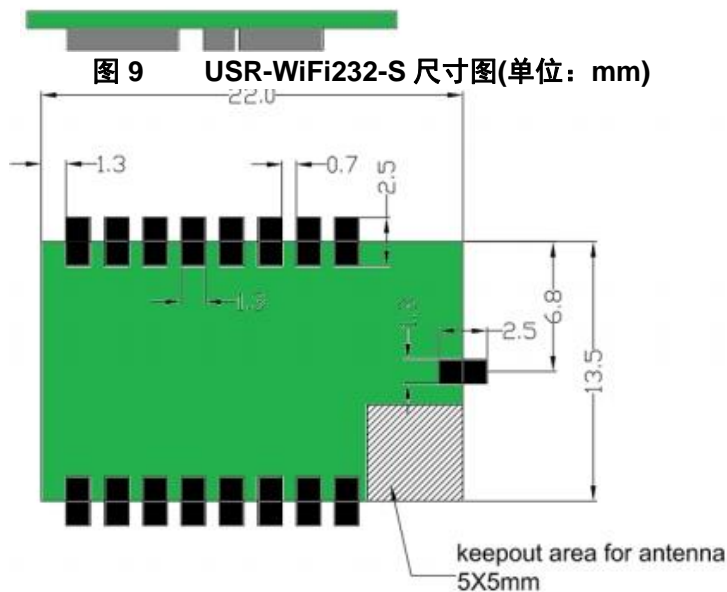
USR-WIFI232-S PCB 元件尺寸 (单位: mm)
